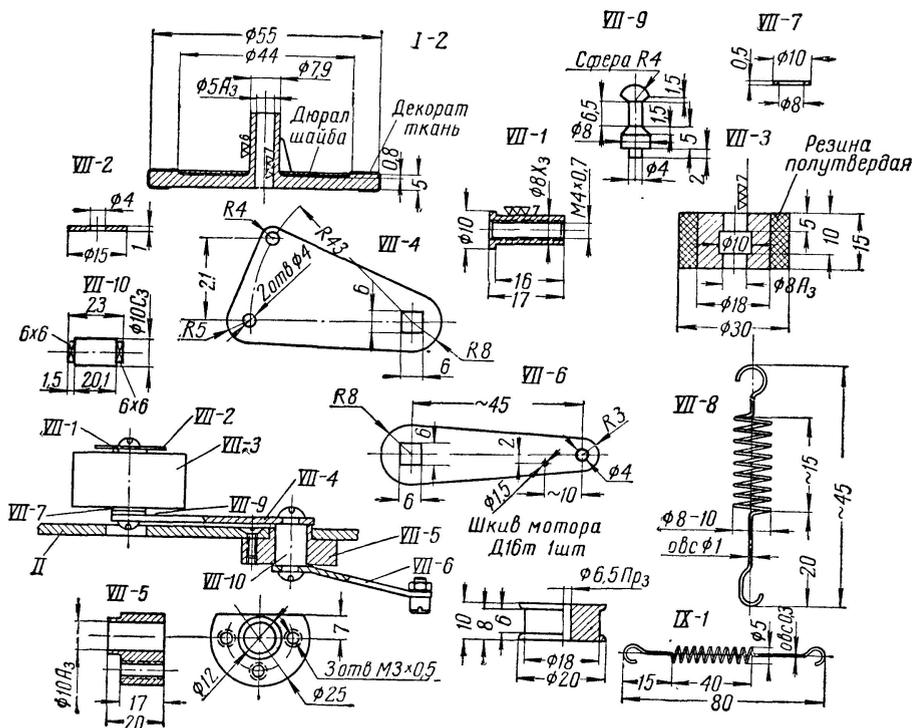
Сборочный чертеж, детали узла прижимного ролика и различные детали. I—2 — 2-й вариант подтарельника — материал сталь или бронза. Декоративная ткань — п.онкий бархат наклеивается клеем БФ-2; VII—1 — ось прижимного ролика — (сталь) (1 шт.); VII—2 — шайба Д16Т (1 шт.); VII—3 — прижимной ролик (1 шт.) — бронза и полутвердая резина Наружную поверхность ролика диаметром 18 накатать, одеть на нее плотно с клеем «88» или без него резиновое кольцо, насадив ролик на оправку проточить резину; VII—4 — рычаг верхний — сталь толщина 2 мм (1 шт.); VII—5 — втулка — бронза (1 шт.); VII—6 — рычаг нижний сталь толщина 2 мм (1 шт.); VII—7 — шайба — бронза или гетинакс (1 шт.) VII—8 — пружина прижимного ролика (1 шт.); VII—9 — направляющая колонка — бронза (1 шт.); VII—10 — Ось поворота — сталь (1 шт.); IX—1 — пружина рычага подвода пленки.
